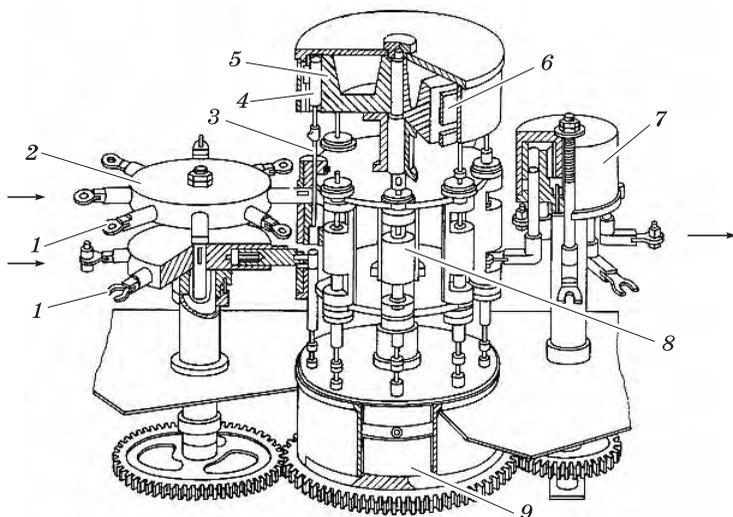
Схема привода рабочих головок роторного сборочного автомата
